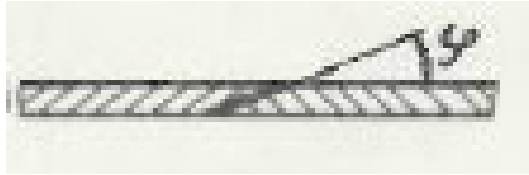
Tupý spoj s vyznačenou tloušťkou spoje [1]
